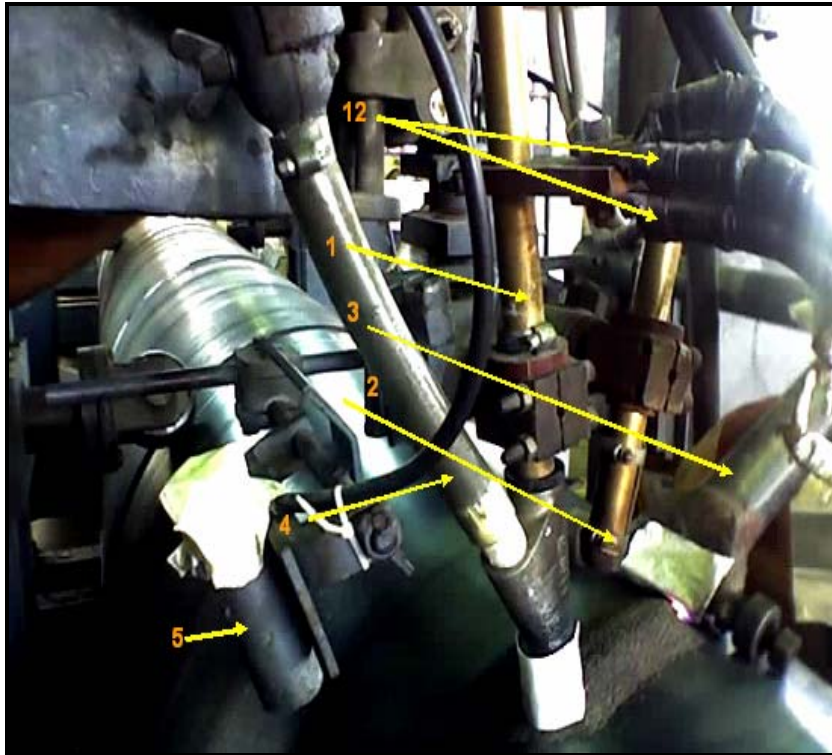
Se observa parcialmente las piezas que integran el cabezal de soldadura con su nombre.
